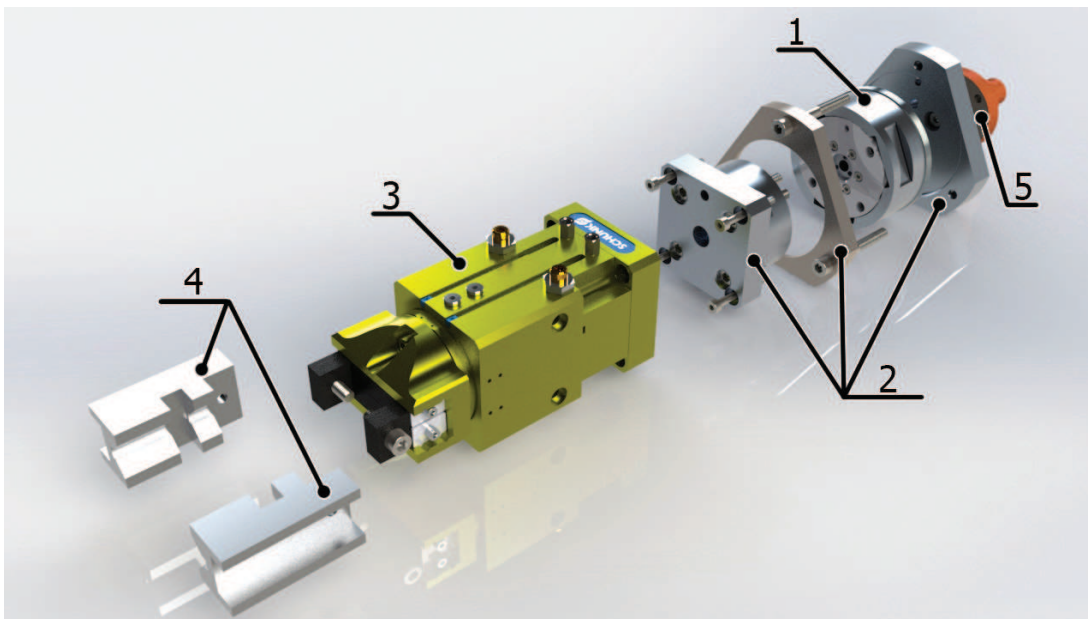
Адаптивное захватное устройство: 1 – силомоментный датчик Gamma SI-65-5, 2 – монтажное приспособление, 3 – пневматический схват Schunk GSM-P 64-E-180, 4 – призматические губки, 5 – выходное звено манипулятора
